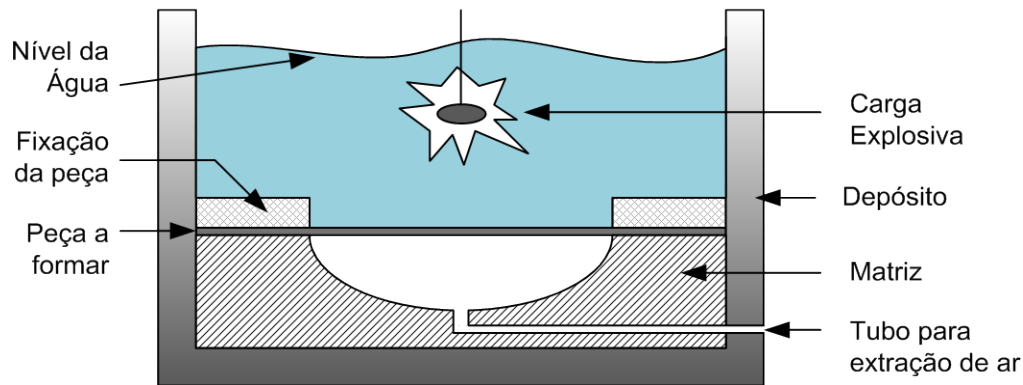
Exemplo de um sistema de moldagem explosiva dentro de água
